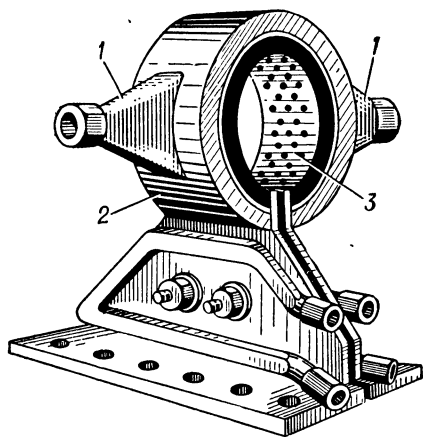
Индуктор для закалки цилиндрич. деталей способом одновременного нагрева: 1 — воронки для выравнивания давления закалочной воды в камере 2; 3 — индуктирующий провод с отверстиями для выхода закалочной воды.
